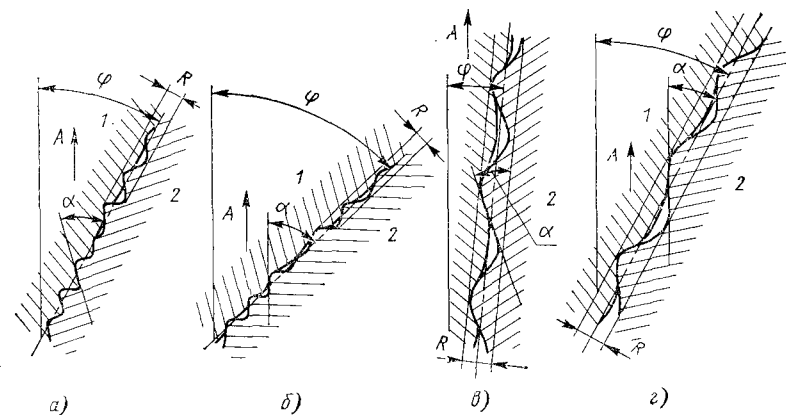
Схема контактирования штампуемой детали с поверхностью штампа
